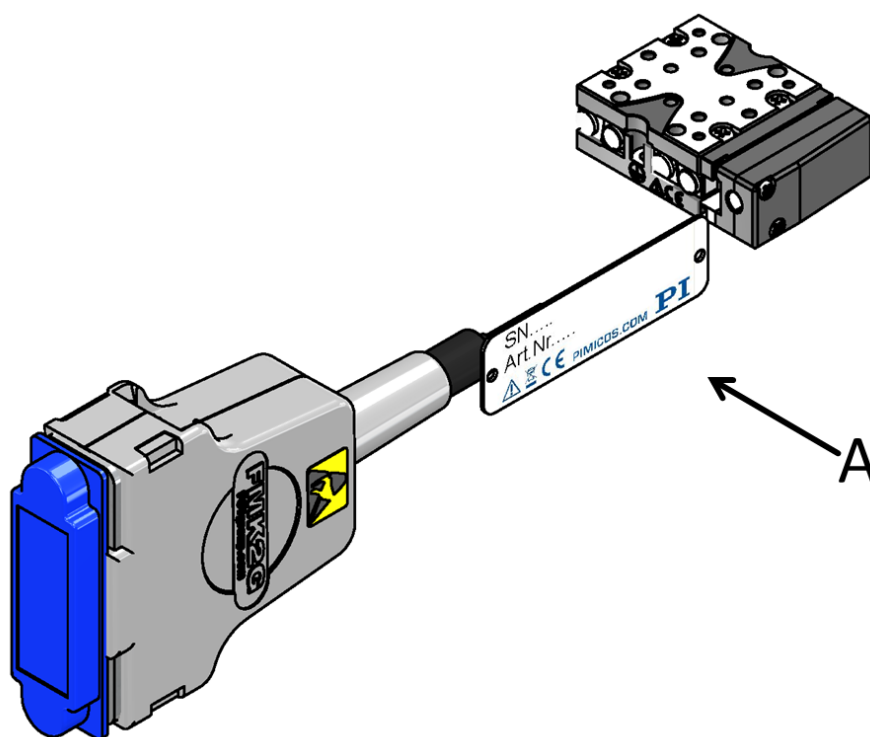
Typenschild des Q-522: Position der Produktbeschriftung (exemplarische Ansicht)
